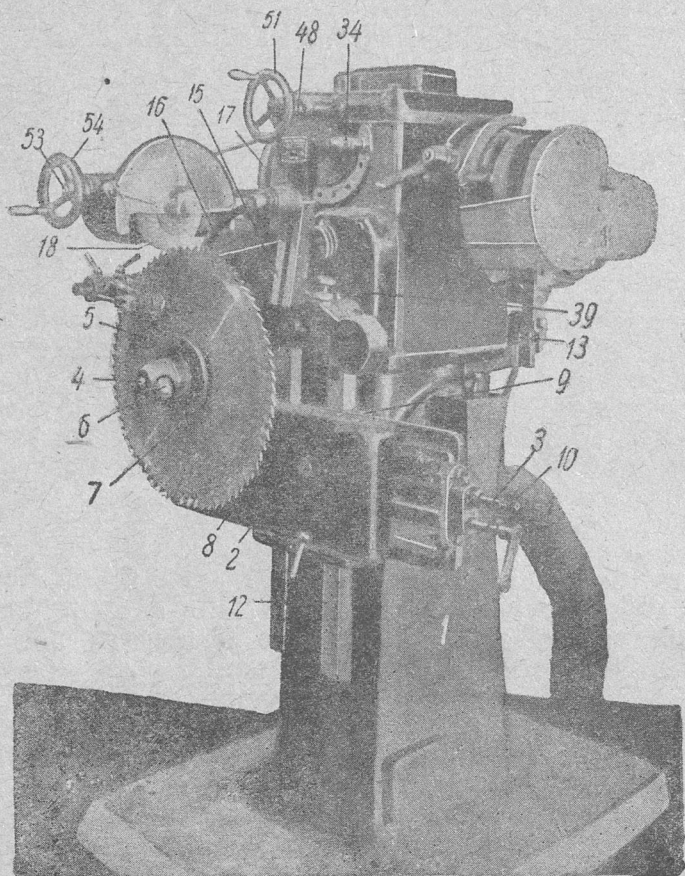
Станок фирмы Геллер для заточки дисковых пил.
